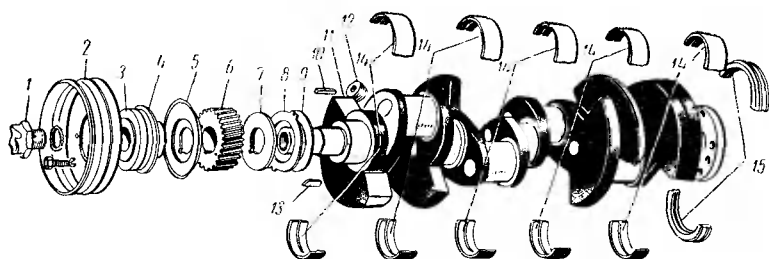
Коленчатый вал двигателя ЗМЗ:
